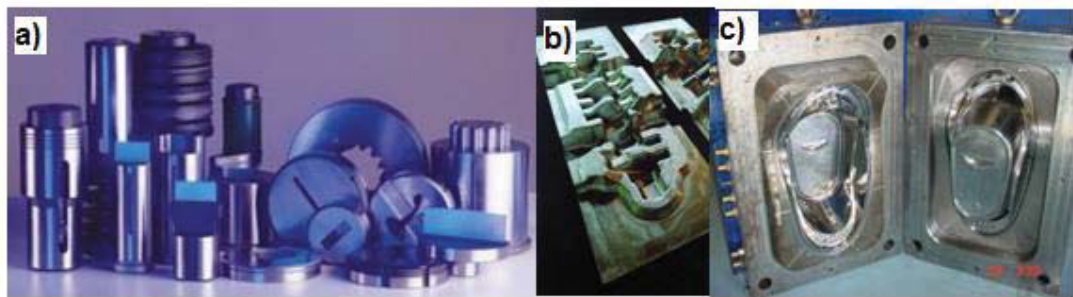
1 Aspecto general de los moldes utilizados en la industria automotriz: a) molde para trabajado en frío, b) molde para trabajado en caliente, y c) molde para inyección de plástico. (Weld mold company 2000).
